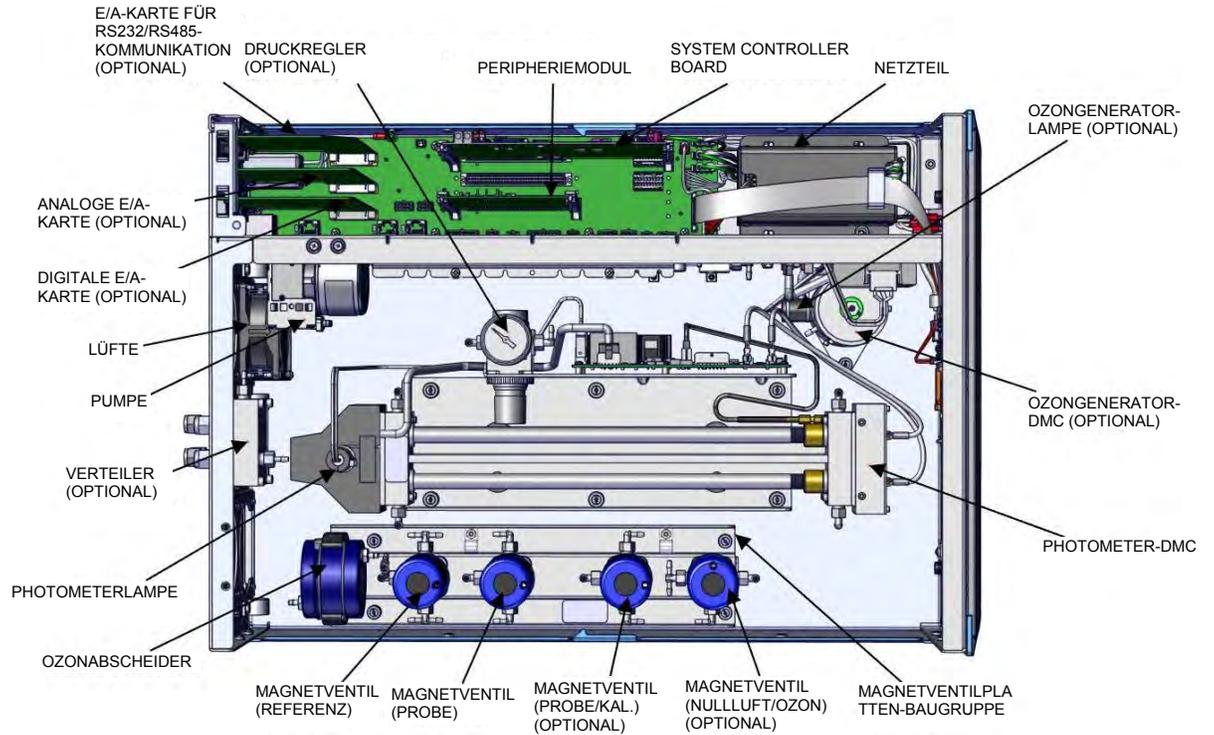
Anordnung der Komponenten des 49iQ – Draufsicht
